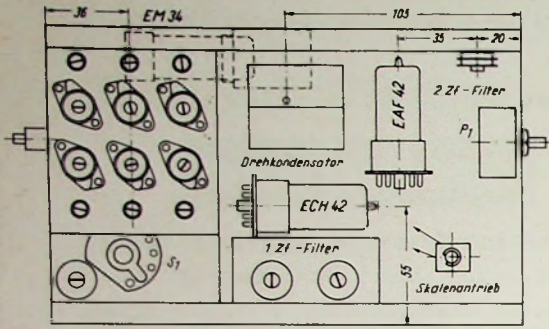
Maßskizze und Einzelteilanordnung für die wichtigsten Bauelemente. Links befindet sich das Spulenaggregat
